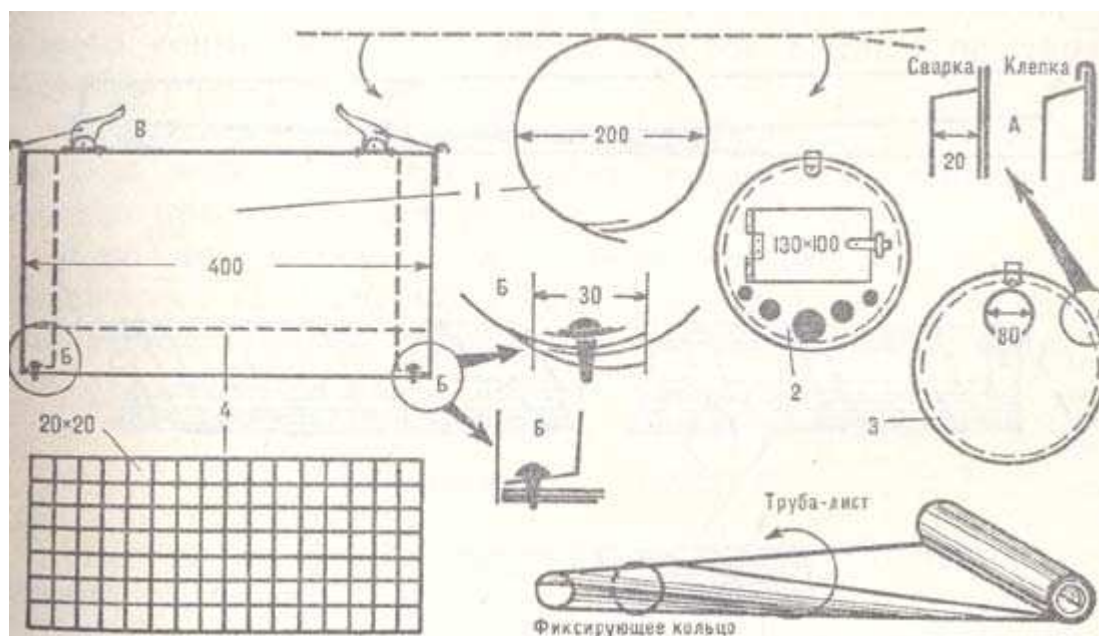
Разборная круглая печь: 1 — цилиндрический корпус; 2, 3 — передняя и задняя крышки; 4 — сетчатый колосник. А — крепление скосов к крышке; Б — соединение цилиндра с крышками; В — крепление верха крышек «лягушками».
